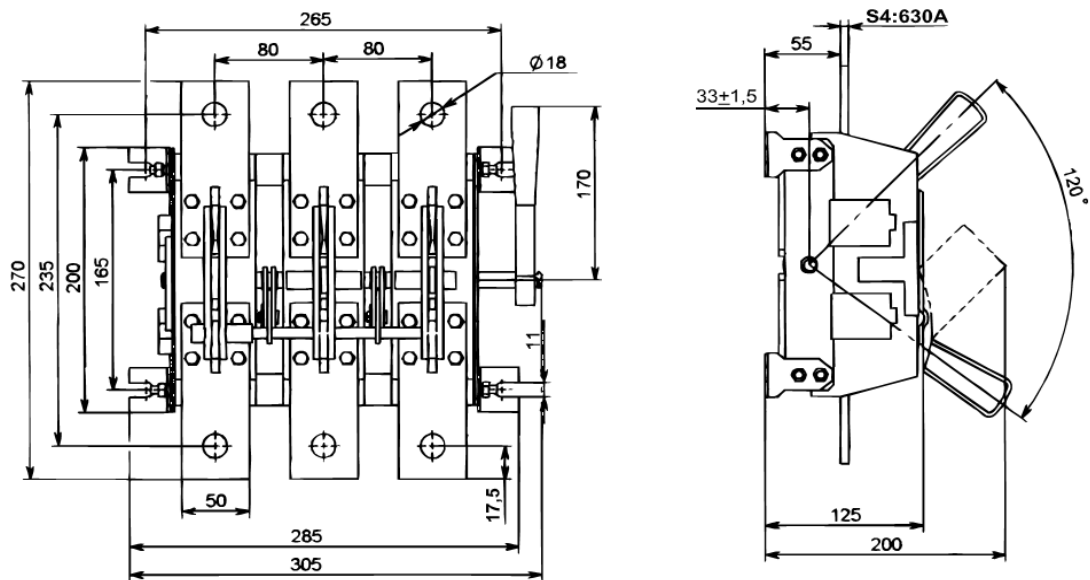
Разъединитель PE19 трехполюсный с боковой рукояткой, переднего присоединения шин
